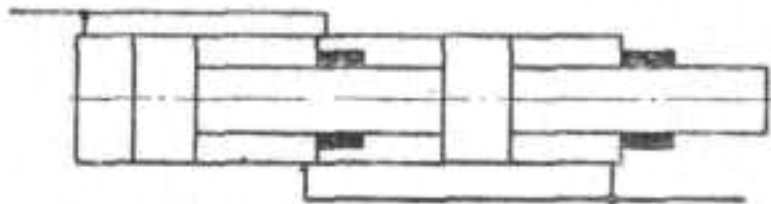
Схема сдвоенного гидроцилиндра
